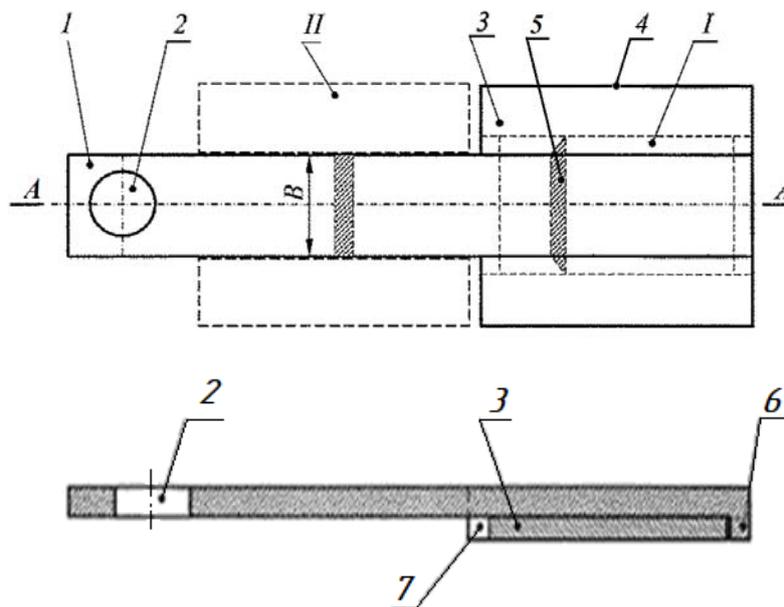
Схема режущего аппарата с жестко связанными ножами
